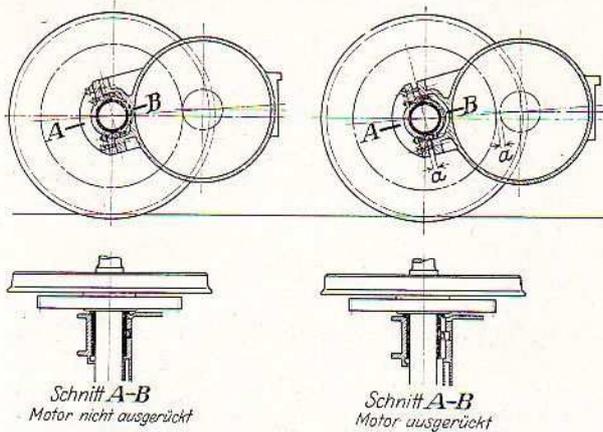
Zeichnung der Vorrichtung zum Ausrücken der Zahnräder.
